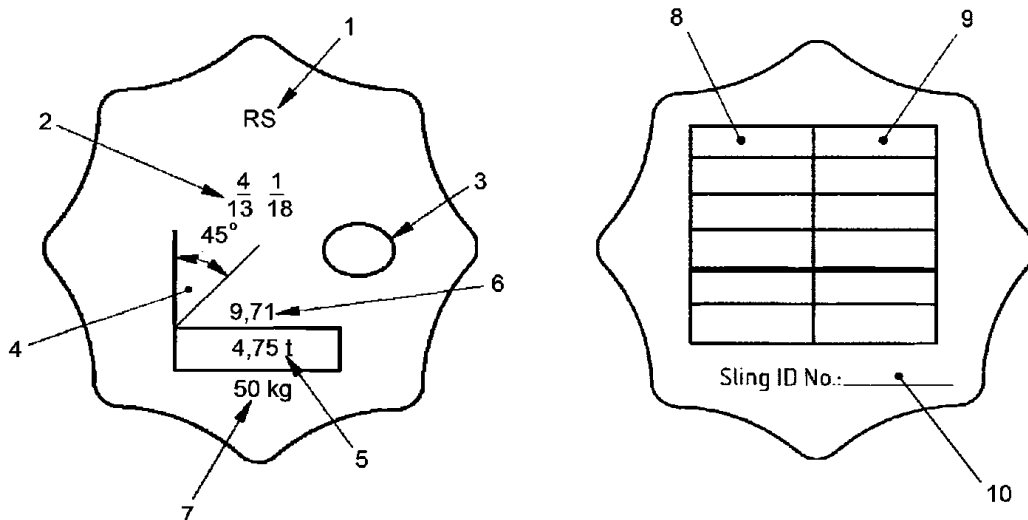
Пример пластины для подъемного приспособления со стропами из цепей:
